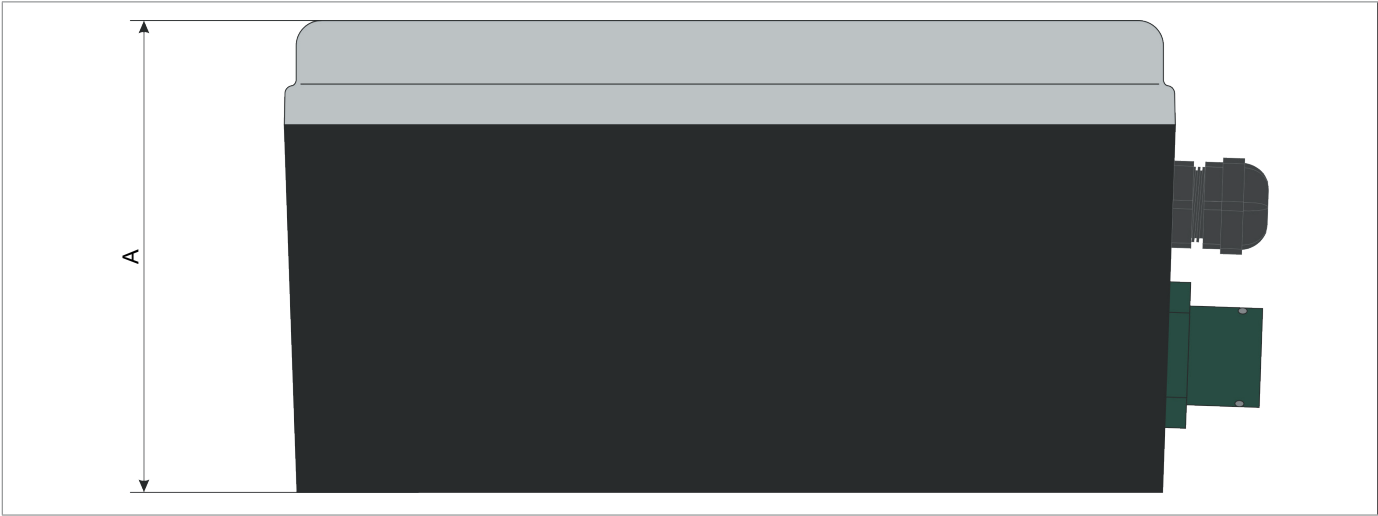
Vista externa lado inferior versión de conector MIL
